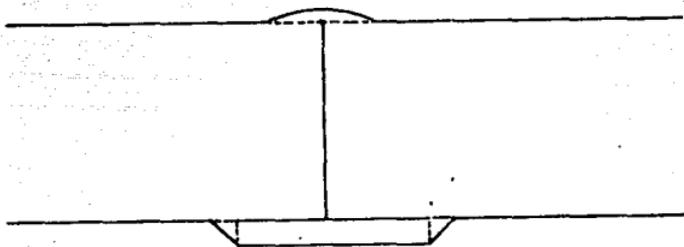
Soldadura Sencilla y Respaldo
